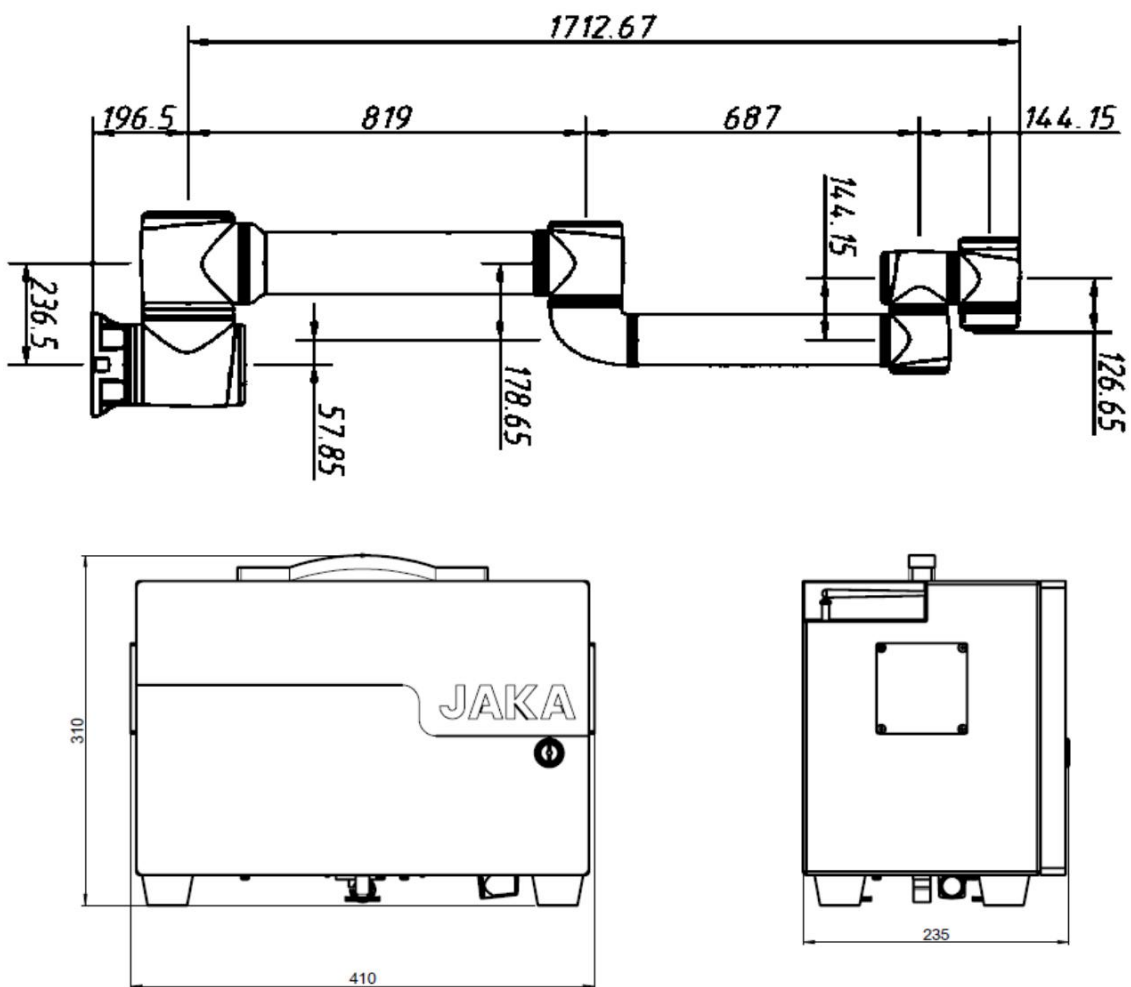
Размеры JAKA Pro 16 и корпуса
